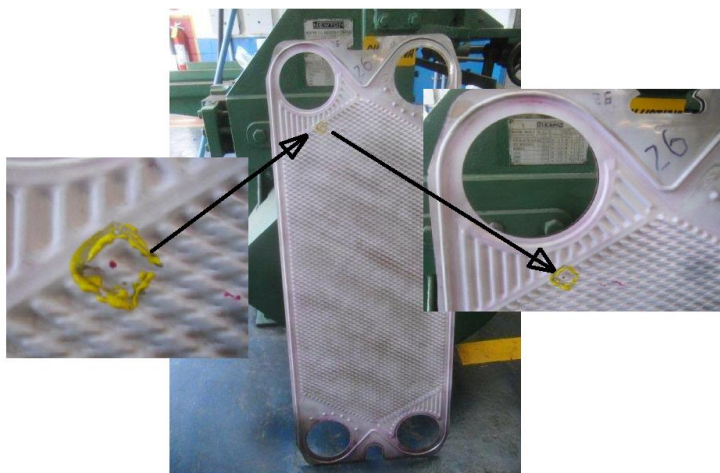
Vista da identificação do dano após ensaio com Líquido Penetrante.
